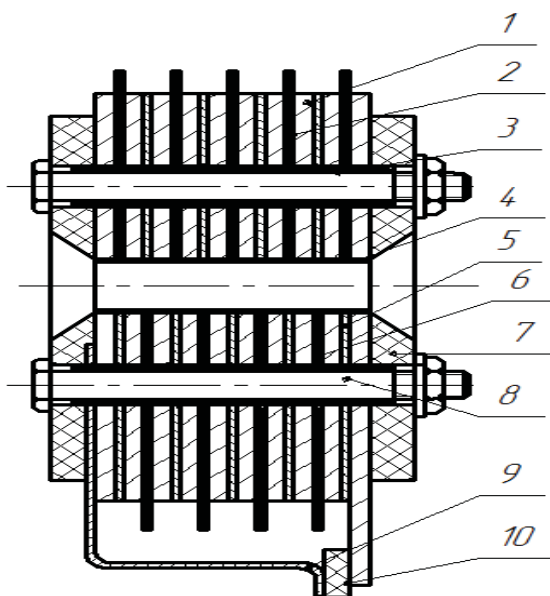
Общий вид пятивиткового пластинчатого индуктора для радиального прессования порошковой композиции: 1 – пластина; 2 – межпластинная изоляция; 3 – изолирующая втулка; 4 – главная изоляция; 5 – закоротка; 6 – межвитковая изоляция; 7 – корпус; 8 – болт; 9 – токовывод; 10 – изолирующая пластина
